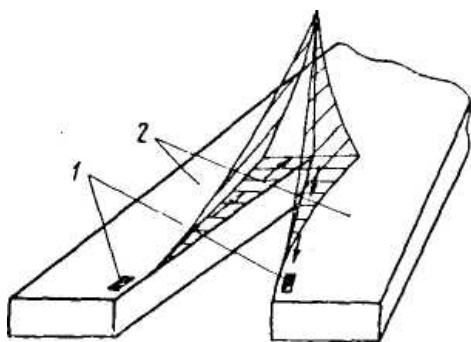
Схема процесса сварки давлением с оплавлением: 1 - место подвода тока; 2 - свариваемые элементы
